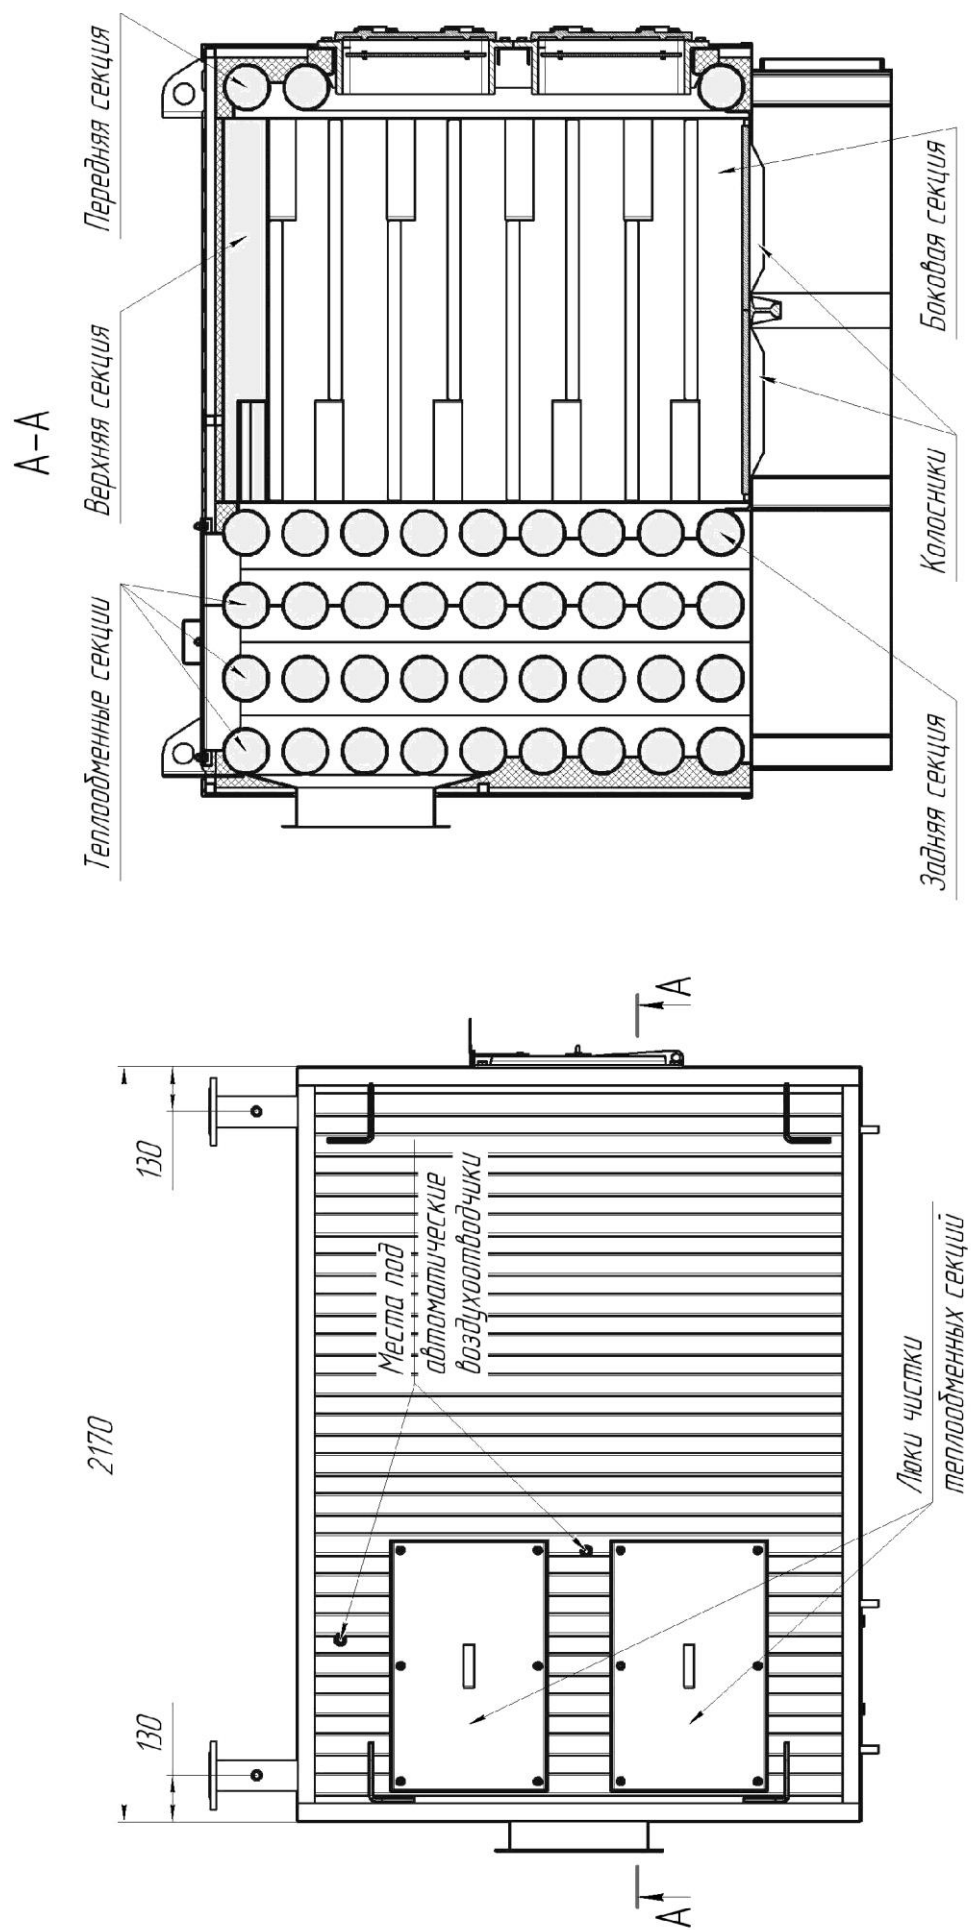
в. Габаритные и присоединительные размеры котла КВр.
